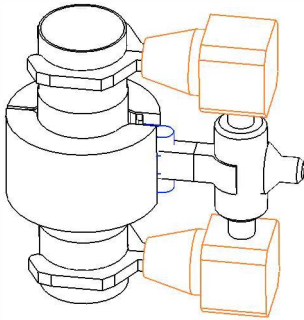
Нагревательное устройство для безлофтового соединения стержней фермы (эффект «памяти формы»)
